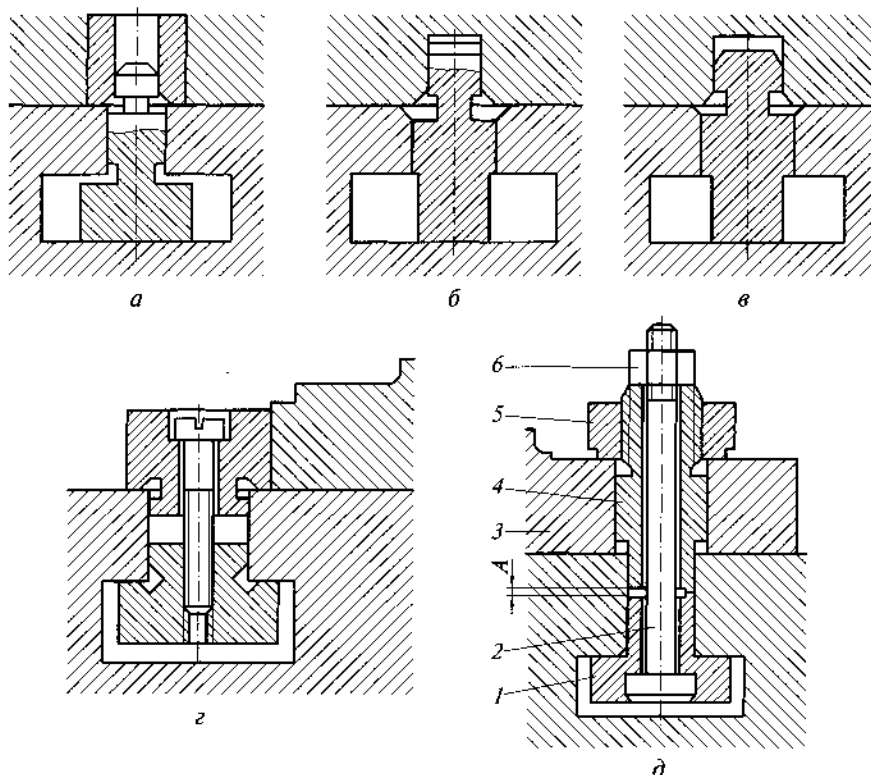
Элементы для установки приспособлений на столе станка (а...д):
